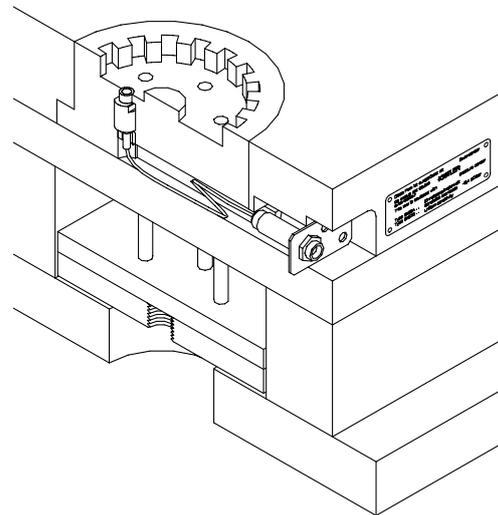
Sensor, Kabel, Stecker, Montageplatte (Mat. Nr. 65005208) und Identifikationsschild
